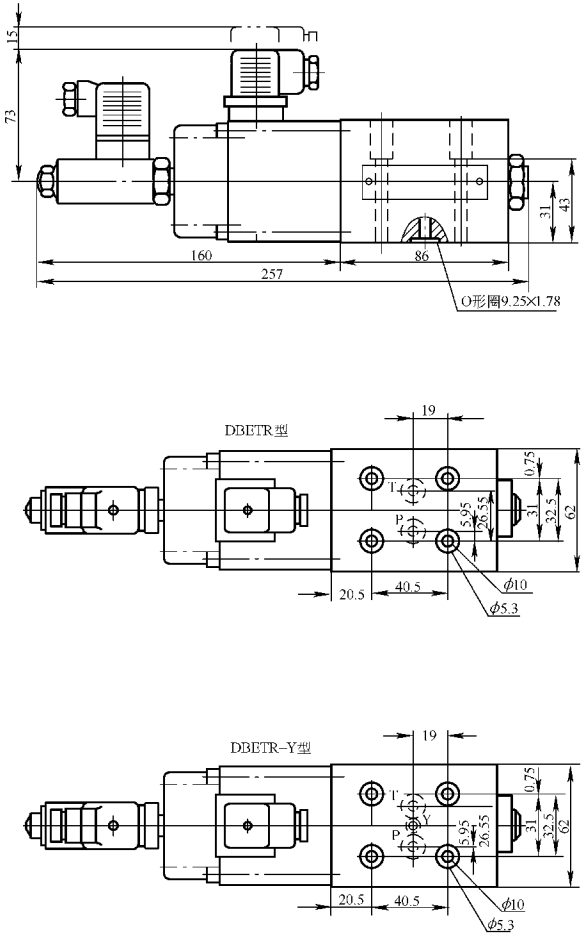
DBETR 型比例溢流阀外形尺寸
